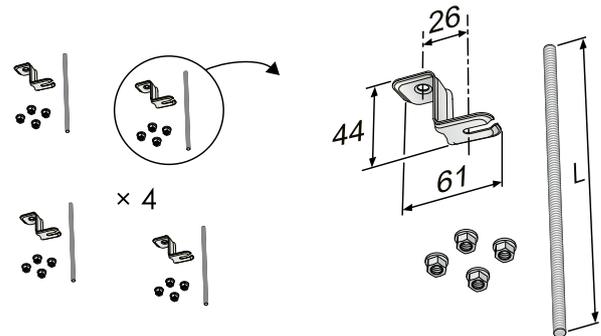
Montageteil SYST MS M8-1, Deckenbefestigung und Gewindestange
